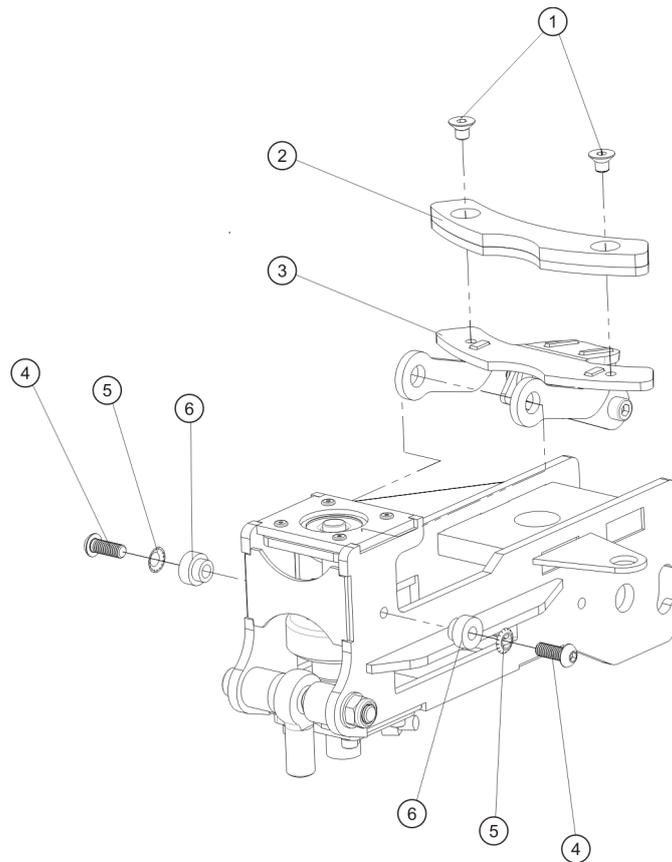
Rotorkopfbrücke mit Rotorbremse
